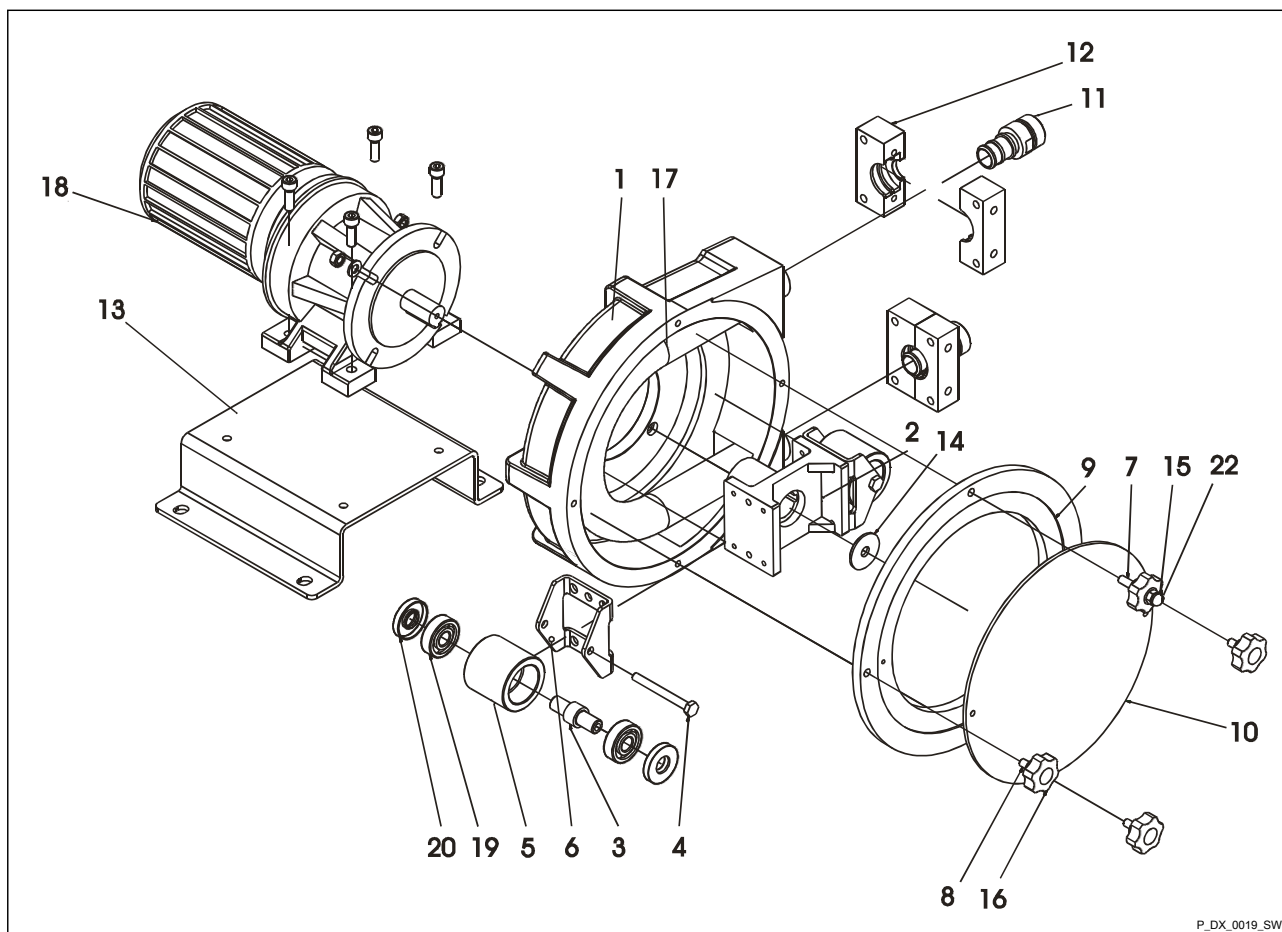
Explosionszeichnung Ersatzteile DFBa 22
